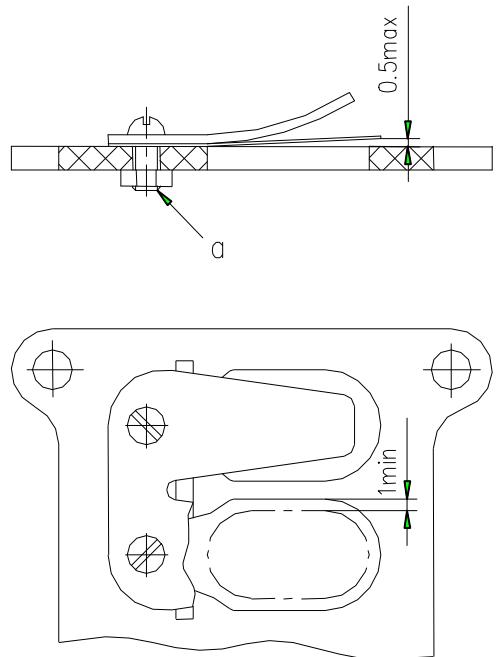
Сборка клапанной перегородки: а - закрепить для контрольки
